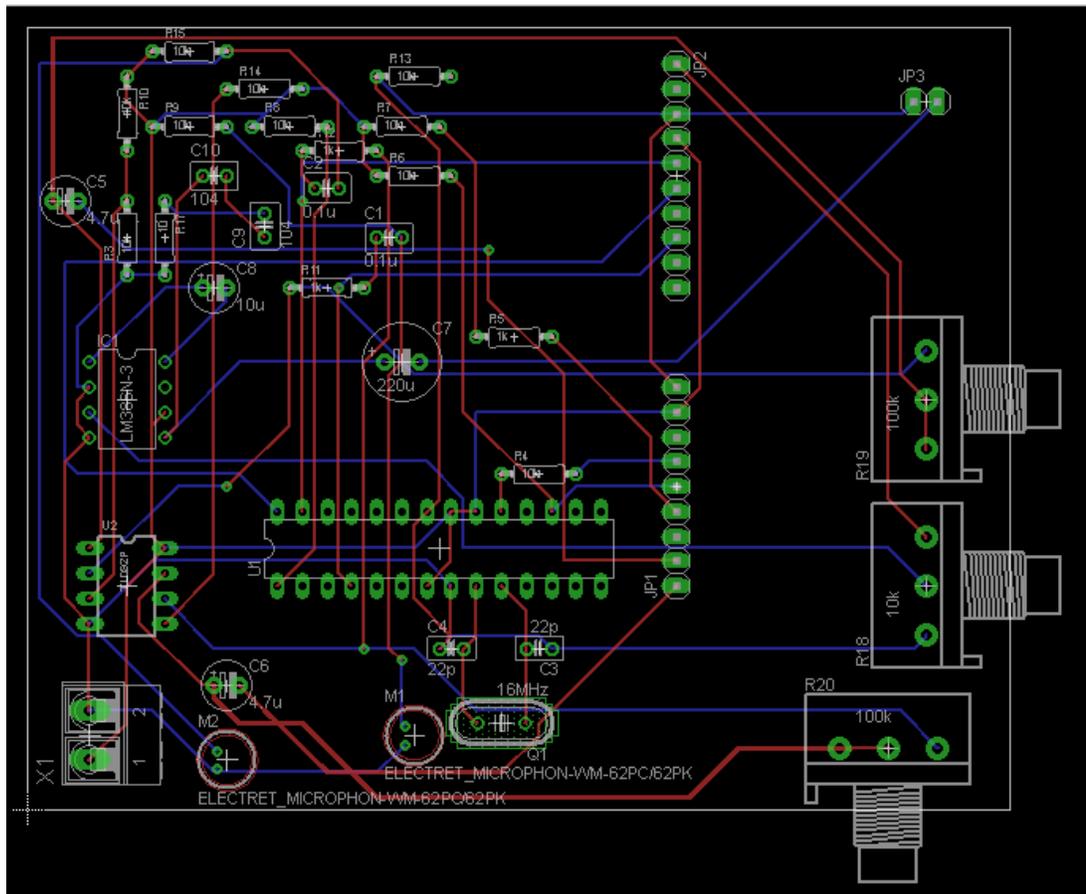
Diseño en EAGLE de la PCB del prototipo de intercomunicador.
